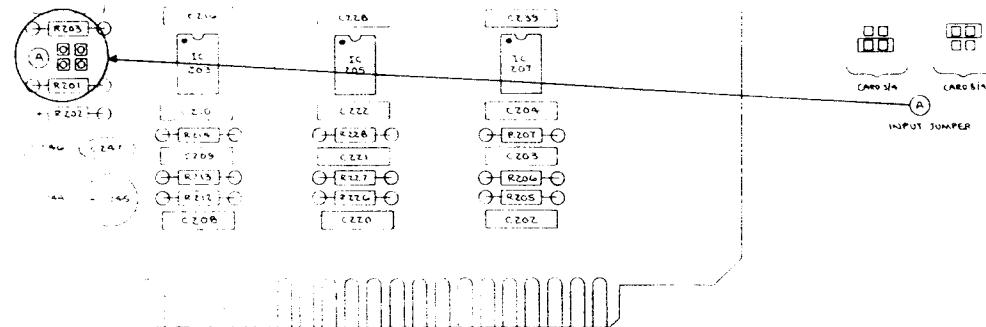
Disposición del de-énfasis para la tarjeta #2
